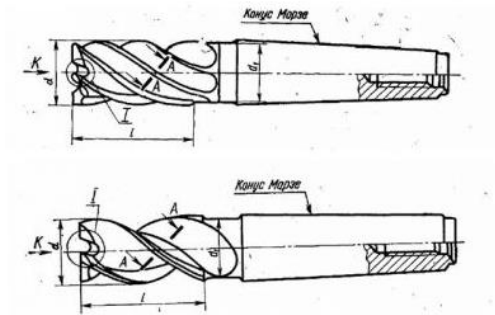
Фреза 2223-0112 P6M5 [ГОСТ 17026-71]
